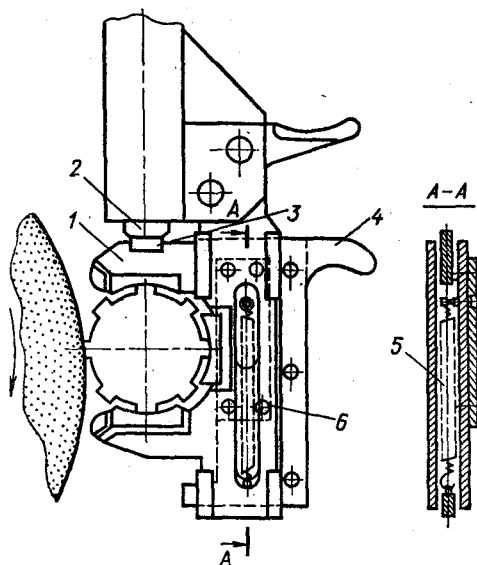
Устройство ЗИЛ для контроля прерывистых поверхностей
